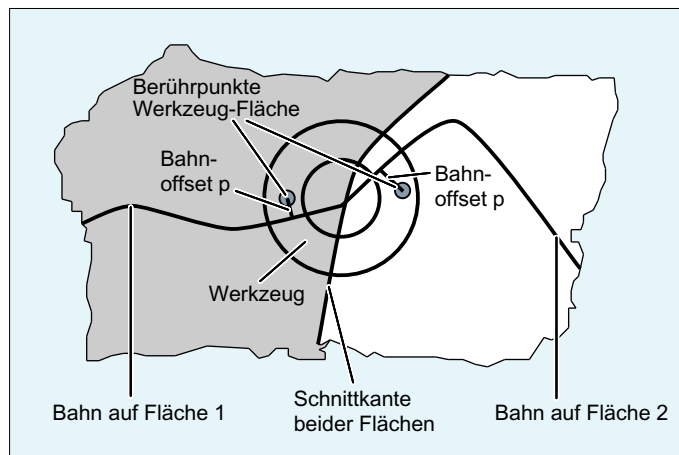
Innenecke beim Stirnfräsen (Ansicht in Richtung der Werkzeuglängsachse)
